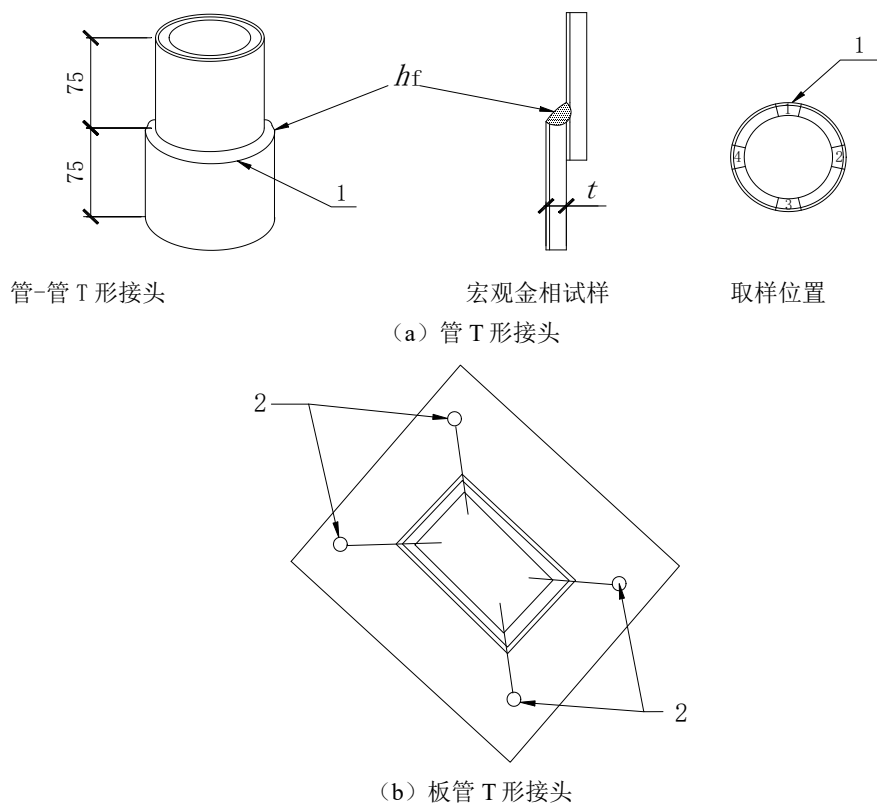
管 T 形和板管 T 形接头焊接工艺评定试件及宏观金相试样取样位置
